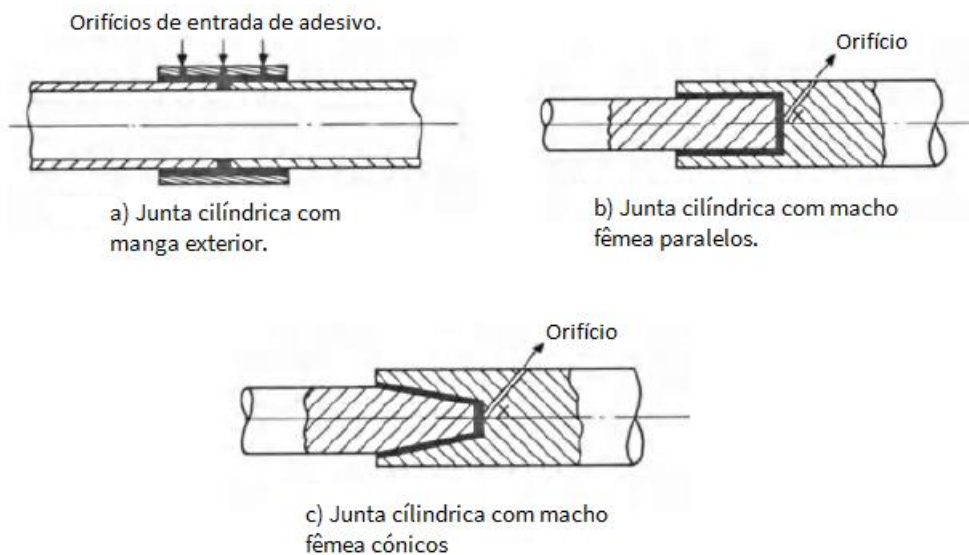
Juntas cilíndricas para tubos e varões sujeitos as esforços axiais ou de torção. Adaptado de *Structural Adhesive Joints in Engineering* [20].
